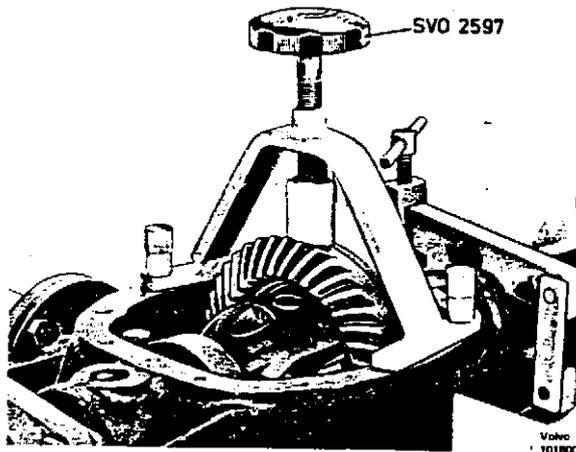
Bremswerkzeug für Ausgleichgetriebe
